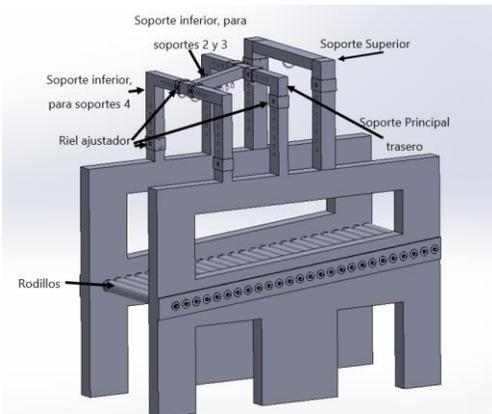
Diseño de caminador con los soportes en SolidWorks
